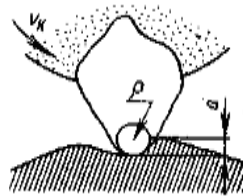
Схема різання абразивним зерном заготовки
